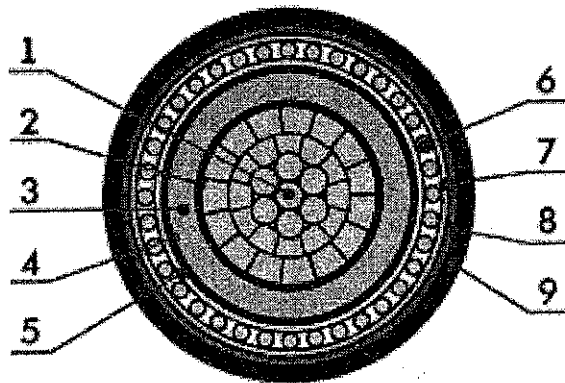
Конструкция одножильного кабеля на напряжение 10-35 кВ:
